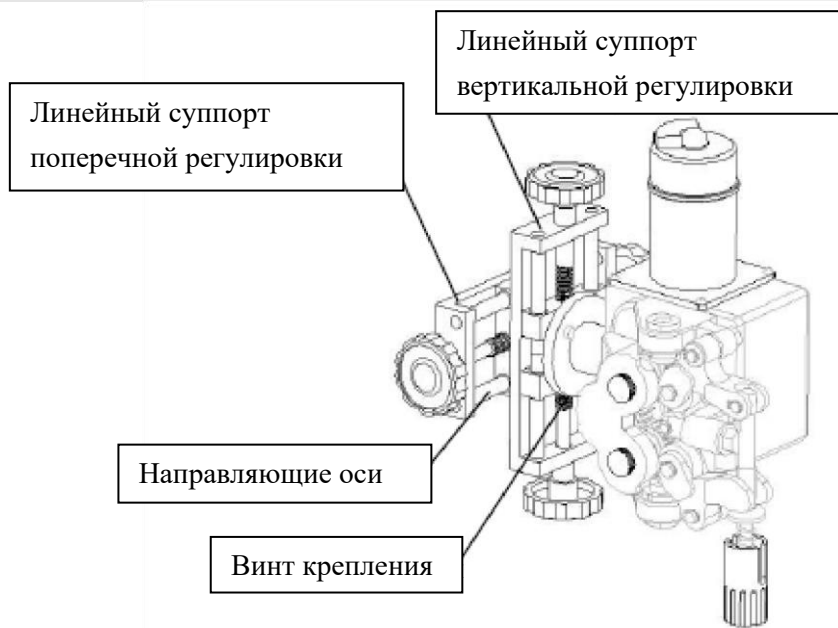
Очистка опорного суппорта сварочной головки
